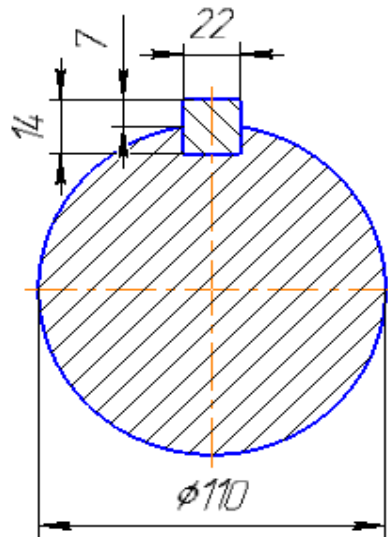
Ескіз шпонкового з'єднання вала з напівмуфтою
